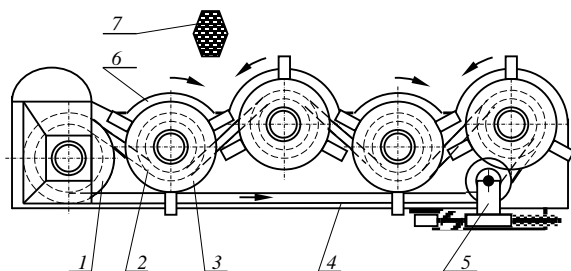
Кинематическая схема рабочего органа косилки с ременным приводом роторов: 1 – ведущий шкив; 2 – ведомый шкив; 3 – ротор; 4 – приводной ремень; 5 – механизм натяжения; 6 – кожух; 7 – сечение ремня
